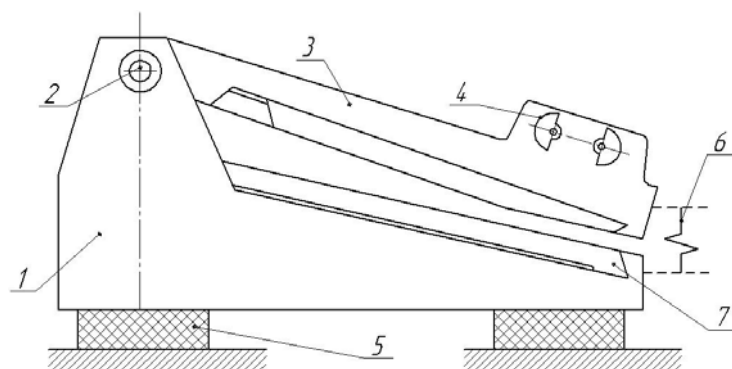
Конструктивная схема виброщёковой дробилки с наклонной камерой дробления
